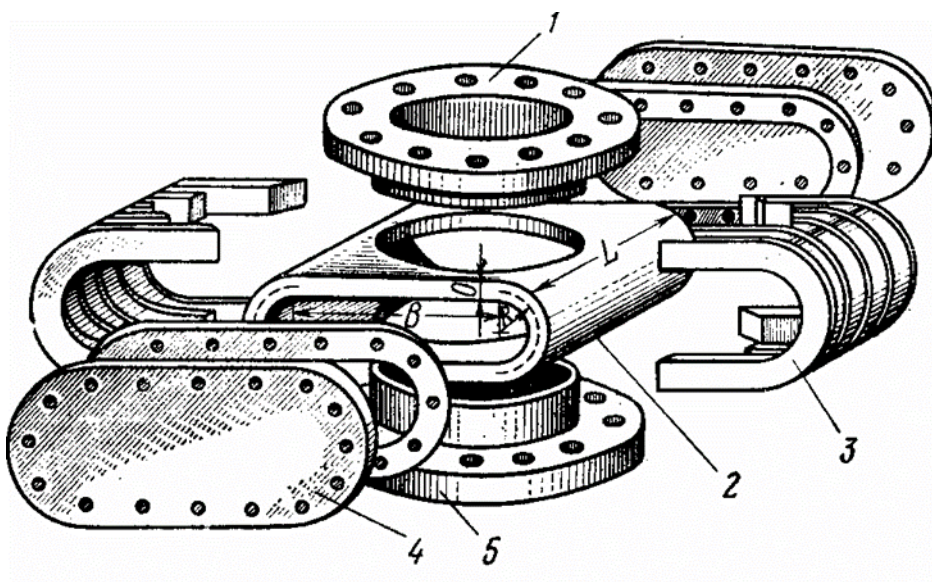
Элементы конструкции корпуса плашечного превентора
